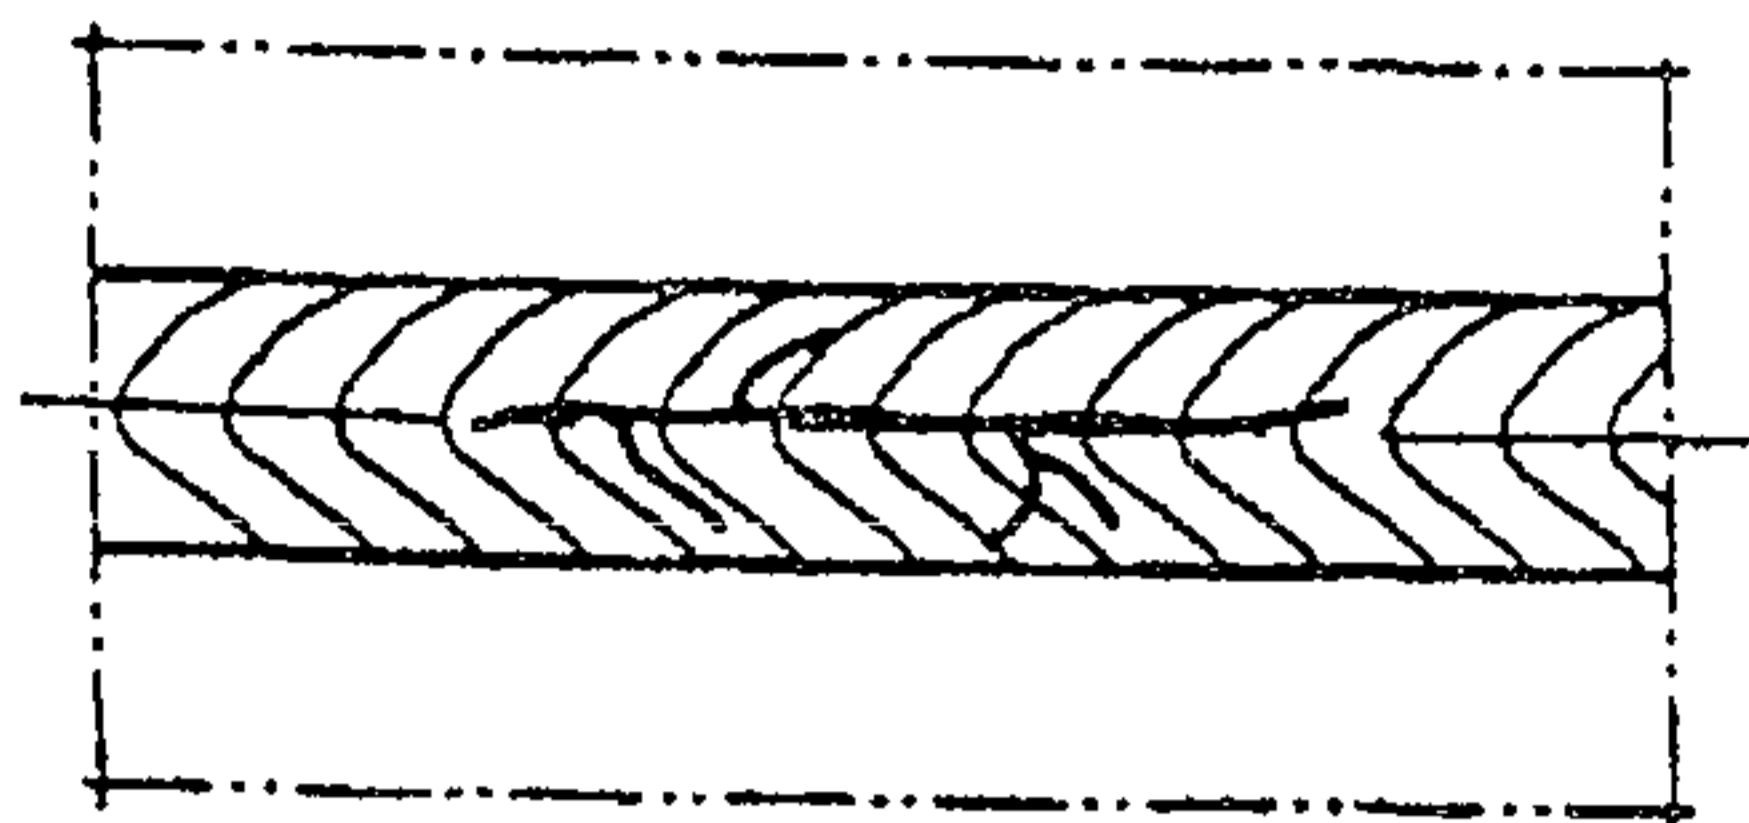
Разветвлённая трещина сварного соединения
